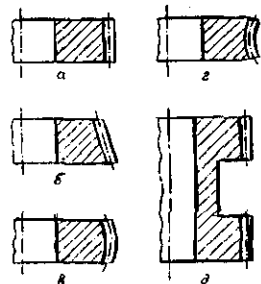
Зубчатые колеса, нарезанные на зубофрезерном станке
